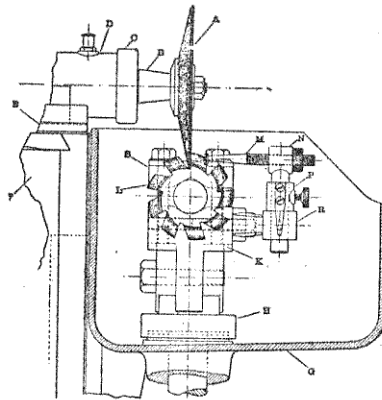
Affûtage d'une fraise de forme à la machine Heald (coupe de l'auge).
